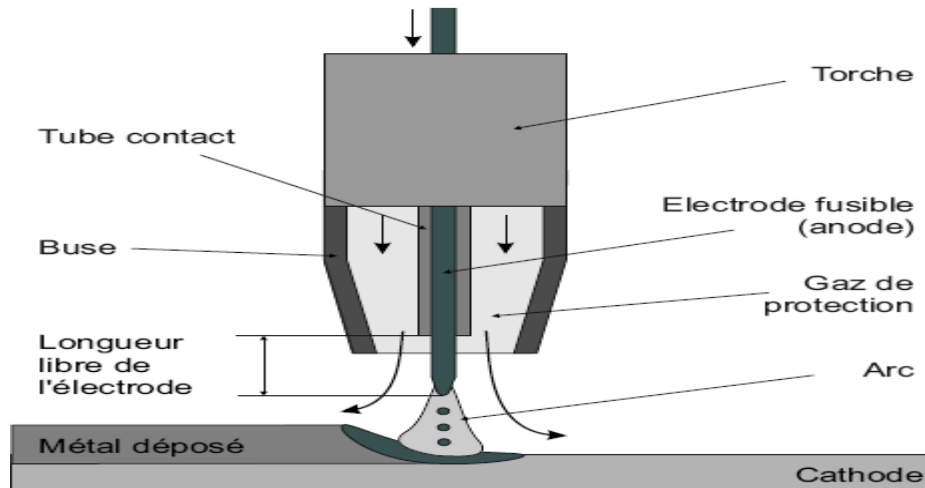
La soudure à l'arc en atmosphère inerte [1].
